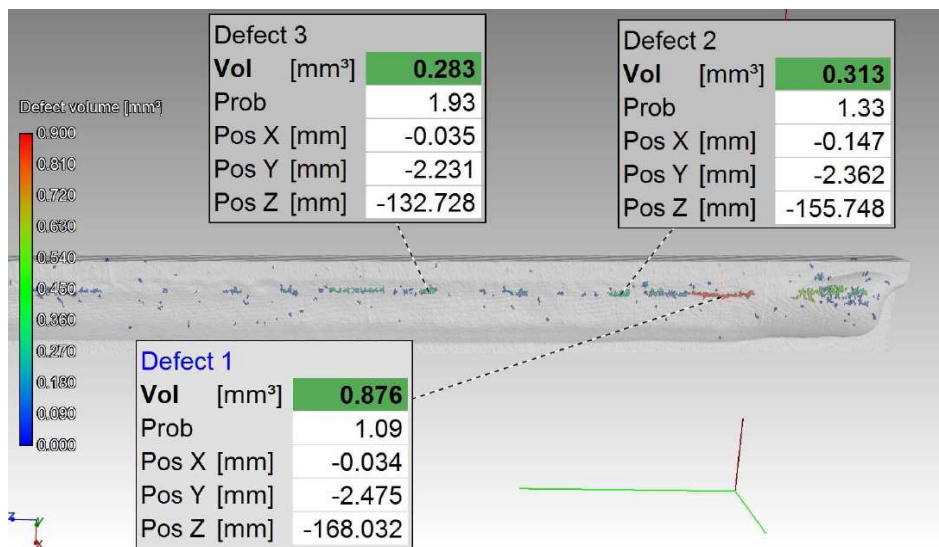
Bildabschnitt C (Schweißnahtanfang) – C.c.58.2
